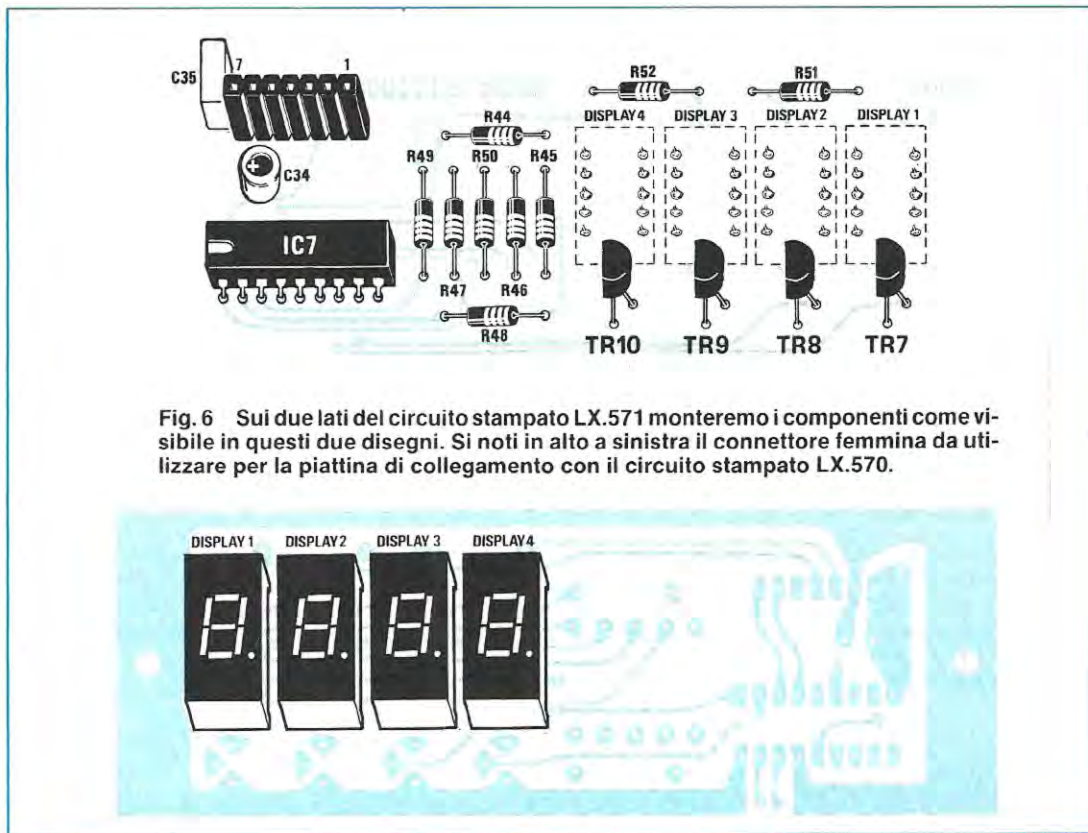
Sui due lati del circuito stampato LX.571 monteremo i componenti come visibile in questi due disegni. Si noti in alto a sinistra il connettore femmina da utilizzare per la piattina di collegamento con il circuito stampato LX.570.
